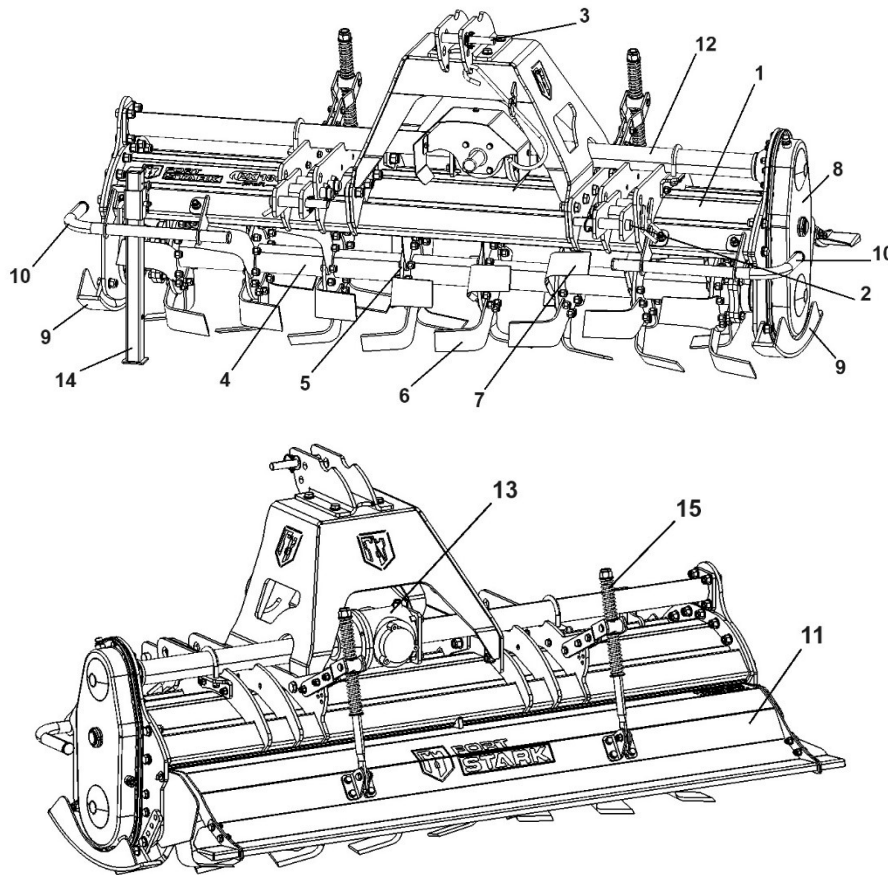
Bodenfräse - allgemeiner aufbau: 1 - rahmen 2 - unterer anlenkpunkt (bolzen) 3 - oberer anlenkpunkt 4 - rotorwelle (fräswelle) 5 - messerflansch 6 - rechtes messer 7 - linkes messer 8 - zahnradgetriebe 9 - gleitkufe 10 - vorderer schutzbügel 11 - heckklappe (prallblech) 12 - zwischenwelle für die kraftübertragung 13 - winkelgetriebe 14 - abstellstütze 15 – federdämpfer
